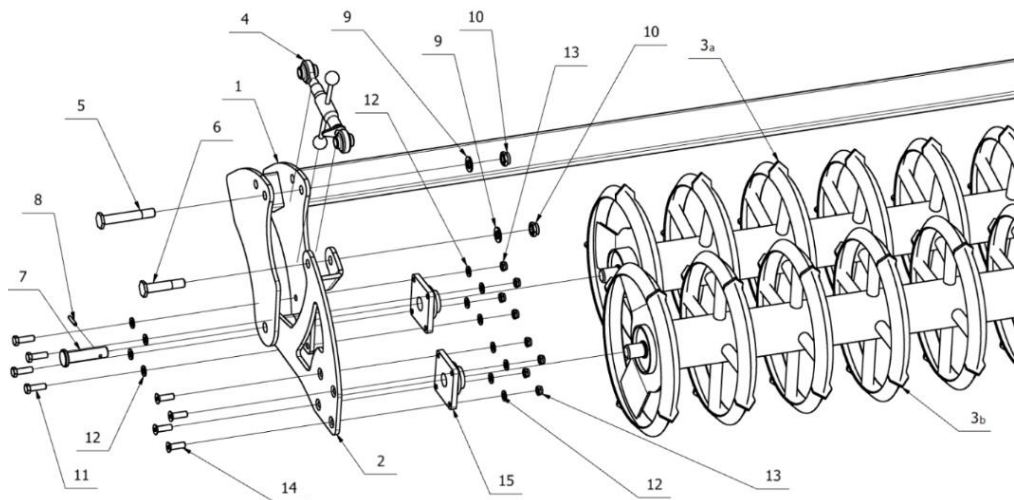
Wał tandem pierścieniowy Ø500mm.
